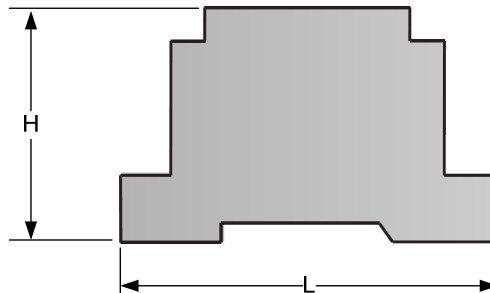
Dimensiones vista superior – Versión STX810-DIN
